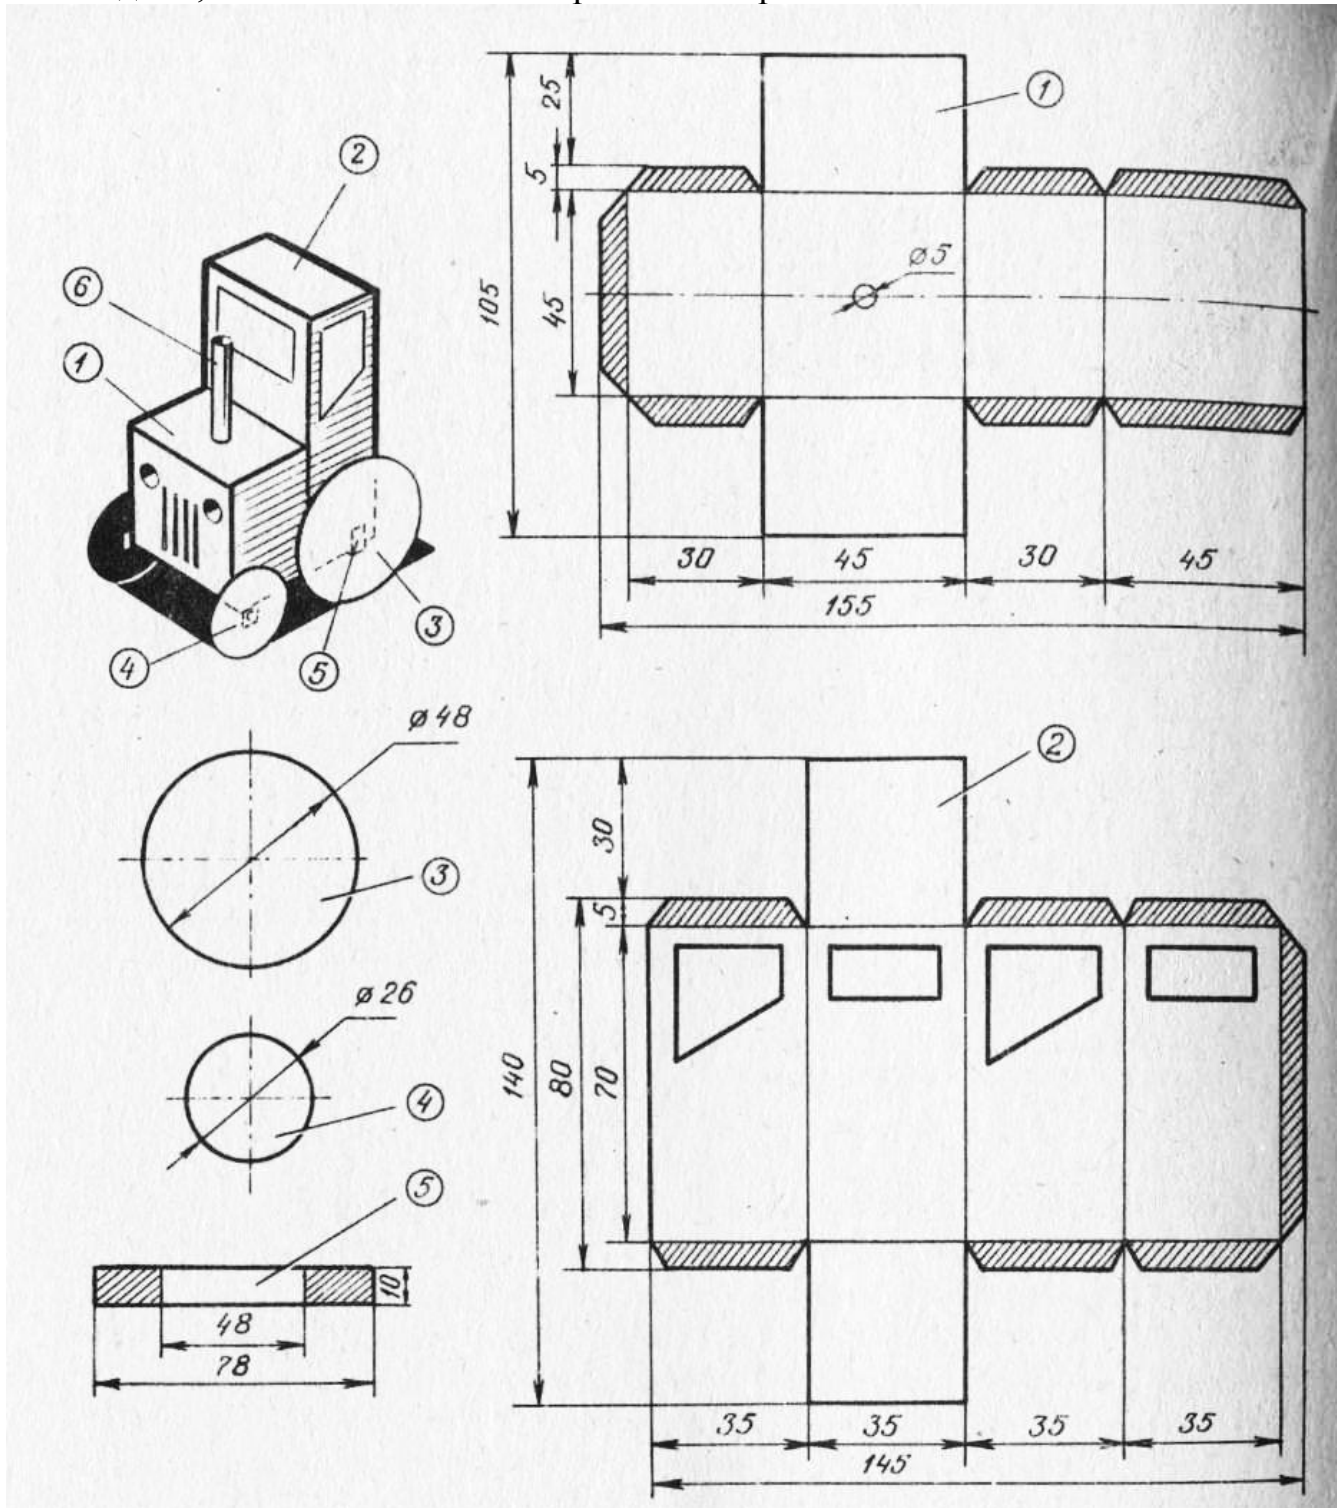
Модель трактора: 1 — капот; 2 — кабина; 3 — заднее колесо; 4 — переднее колесо; 5 — подшипник; 6 — выхлопная труба
